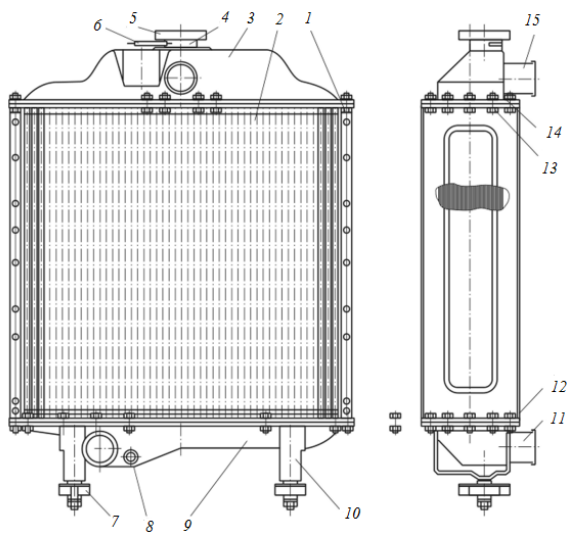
Водяной радиатор трубчато-пластинчатый сборной конструкции: 1 – опорная стойка; 2 – сердцевина; 3 – бачок верхний; 4 – горловина заливная; 5 – пробка заливная; 6 – паровоздушная трубка; 7 – амортизатор; 8 – отверстие сливного краника; 9 – бачок нижний; 10 – опора; 11 – патрубок нижнего бачка; 12 – монтажная пластина; 13 – болт крепежный; 14 – прокладка; 15 – патрубок верхнего бачка
